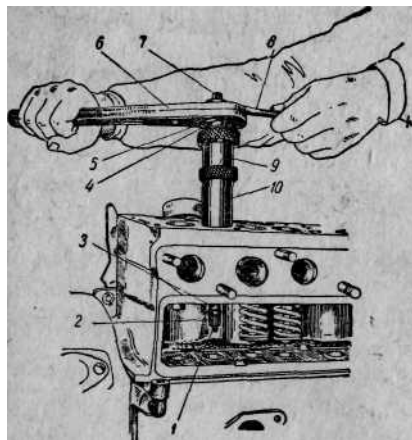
Приспособление для выпрессовки и запрессовки направляющих втулок клапанов.
